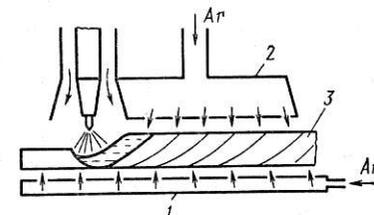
Горелка с удлиненной насадкой для аргонодуговой сварки титана
